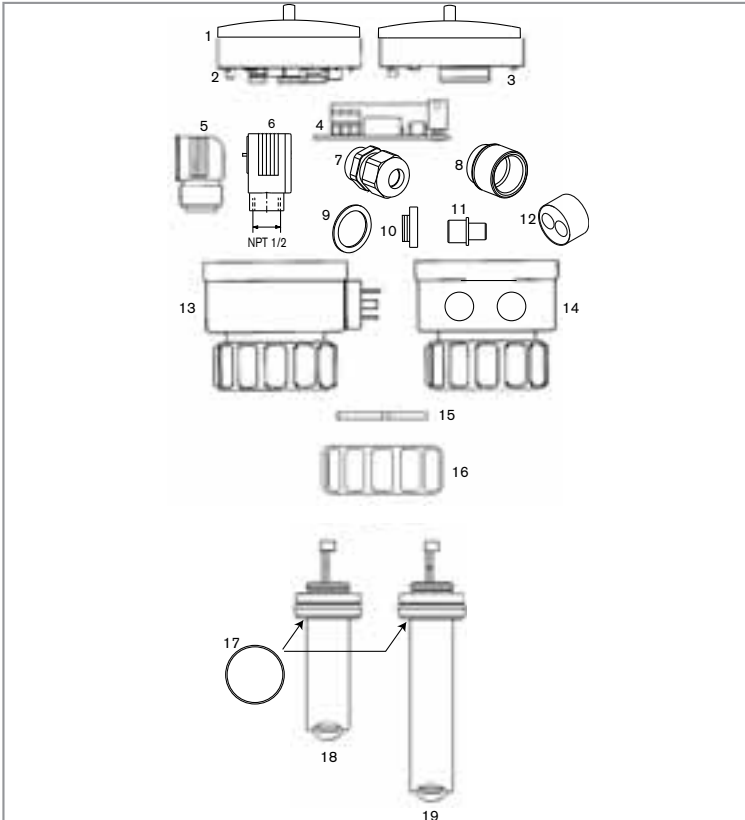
Ersatzteil-Explosionszeichnung, kompakte Ausführung
